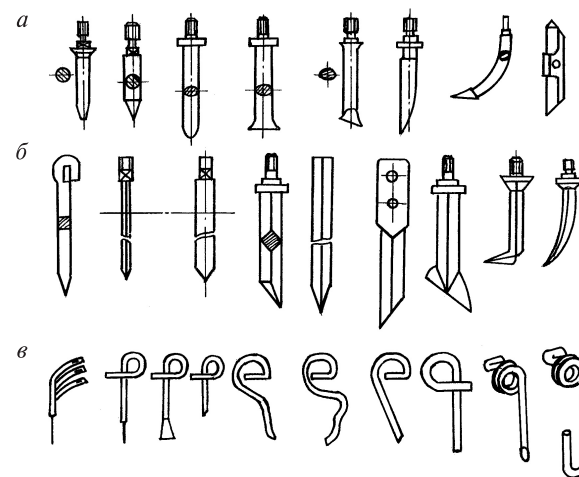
Конструкции рабочих органов зубовых борон: а — зубья круглого и эллипсовидного сечения; б — зубья многоугольного сечения; в — пружинные зубья
